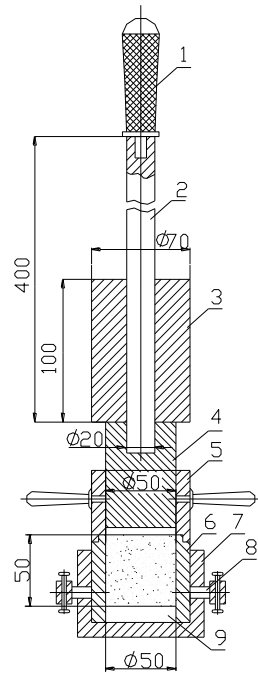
Малий прилад СоюздорНИИ для стандартного ущільнення: 1 – рукоятка; 2 – напрямний стержень; 3 – гиря; 4 – плунжер; 5 – напрямний насадний циліндр; 6 – розбірний циліндр; 7 – підскляник; 8 – закріплючі гвинти; 9 – металева пластинка.
